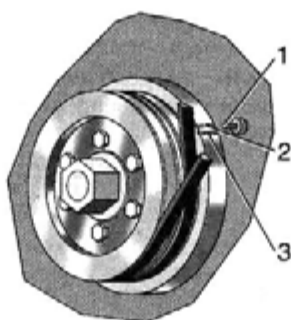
Установочные метки на шкиве-демпфере коленчатого вала:
